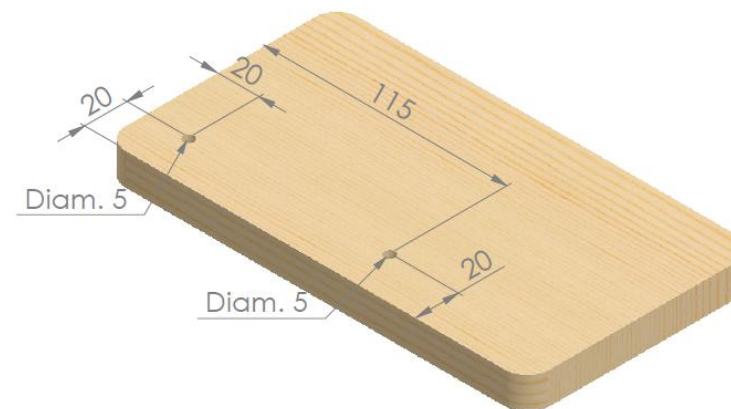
Fixação da chapa de apoio para os braços - Passo 1
